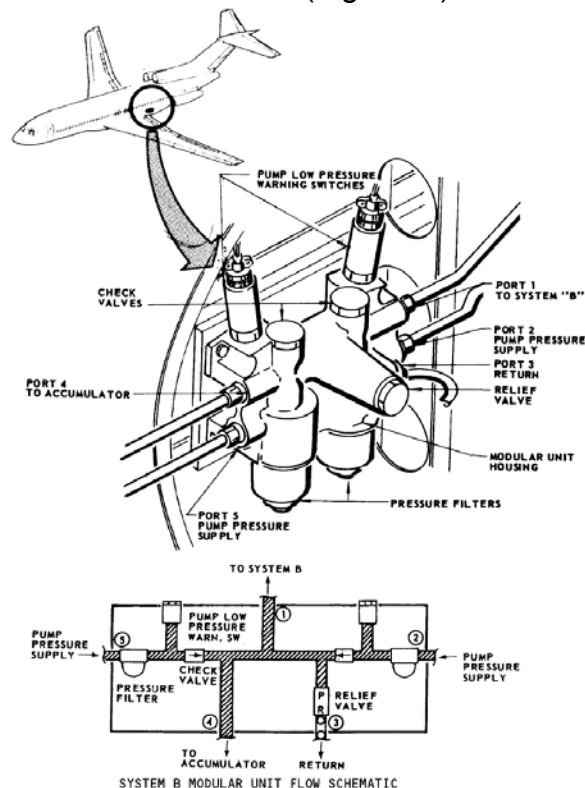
Unidad Modular – Sistema B (Fuente: B727-AMM)
